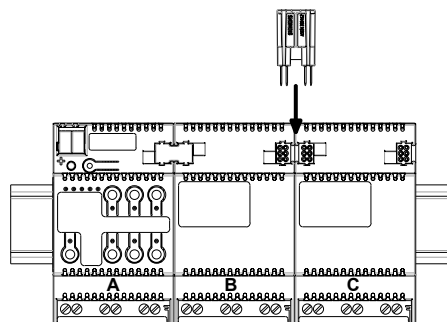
Anschließen einer Schaltaktor-Erweiterung
